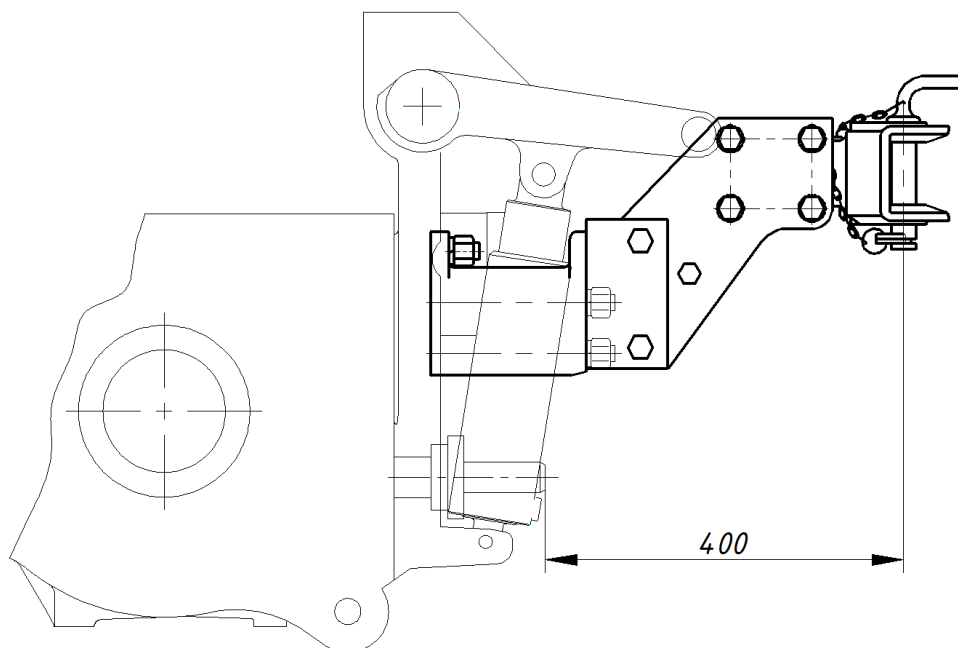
Схема расположения вилки вращающейся неавтоматической
